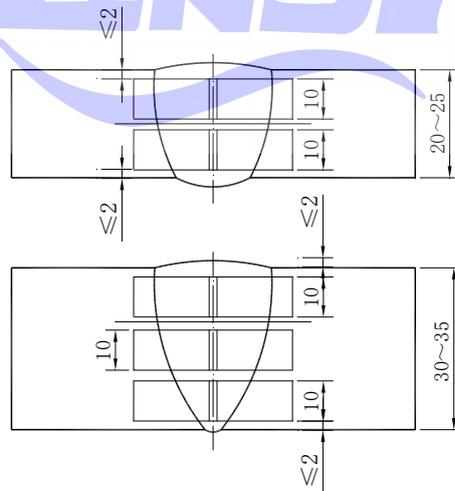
单面焊接双面成型焊接试件的取样位置
